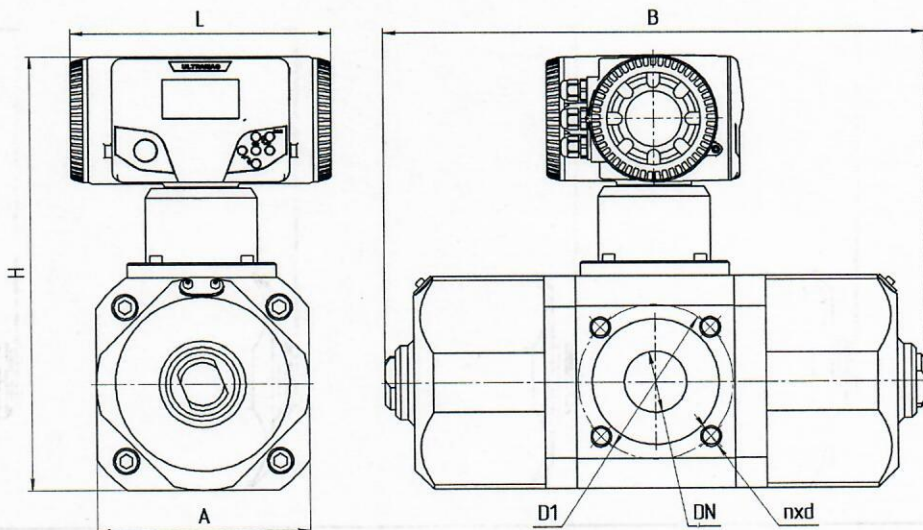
Габаритно-присоединительные размеры комплексов исполнения RT (см. таблицу 6)
